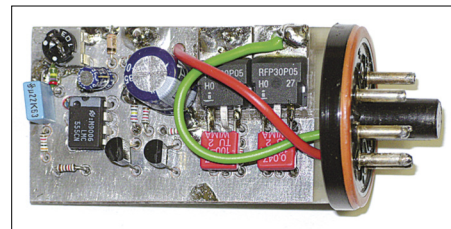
Der elektronische Zershacker lässt sich auf den aus einer defekten Zershackerpatrone gewonnenen Sockel löten und so bequem in die Schaltung einstecken.
